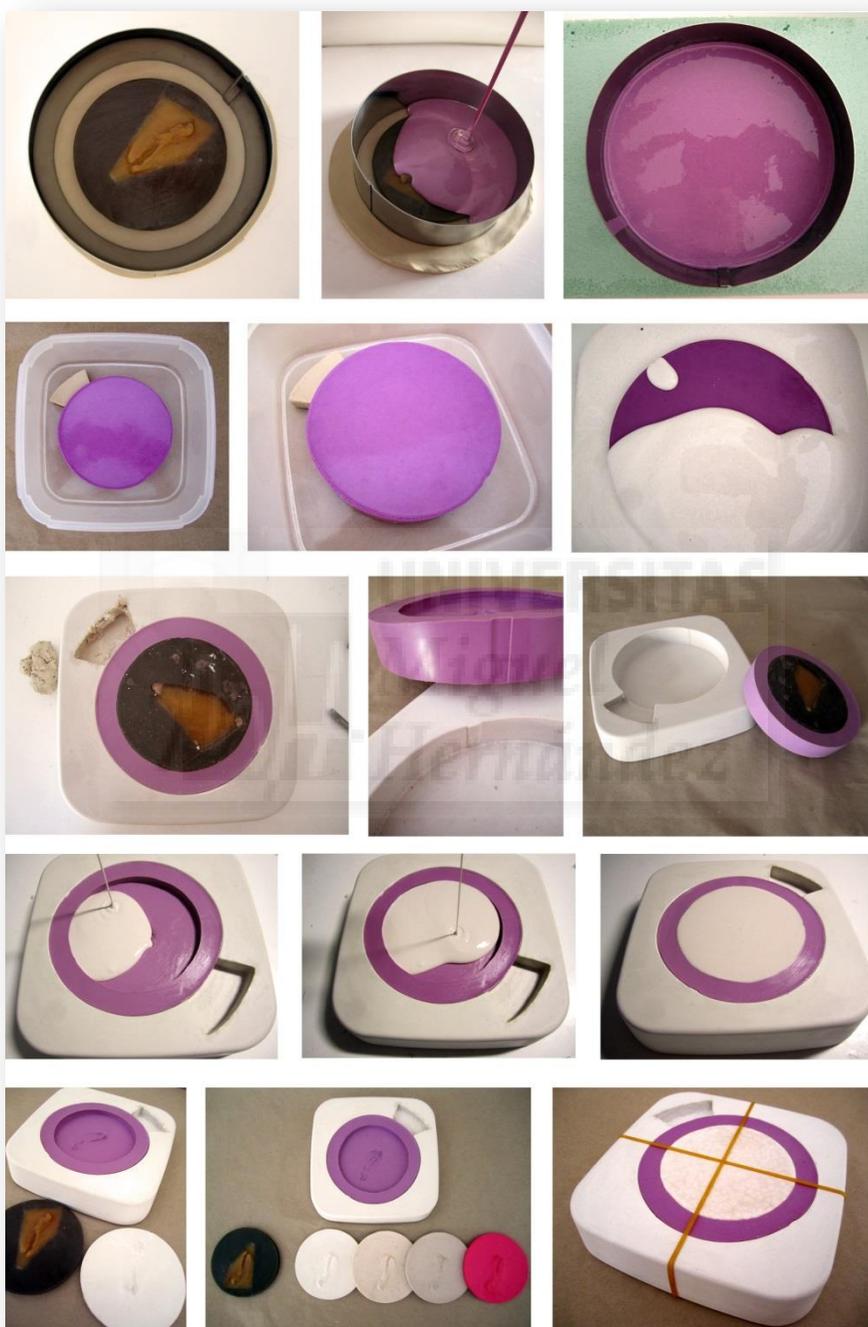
Molde reutilizable flexible de un fragmento por caja.
